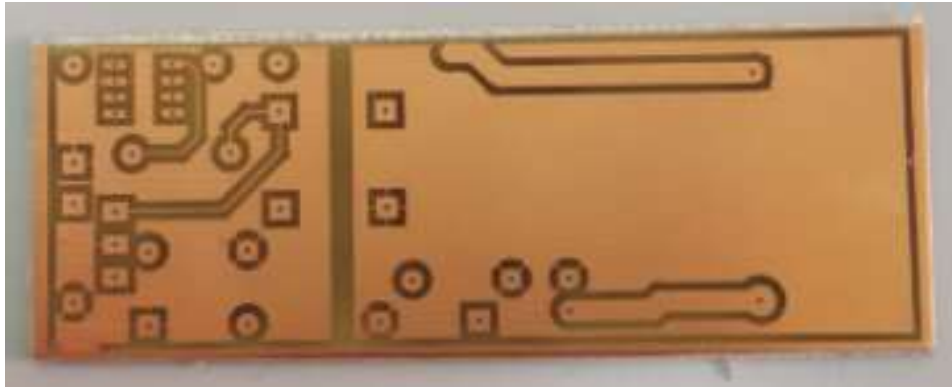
Placa PCB construida sin taladrar y sin componentes (capa BOT)
